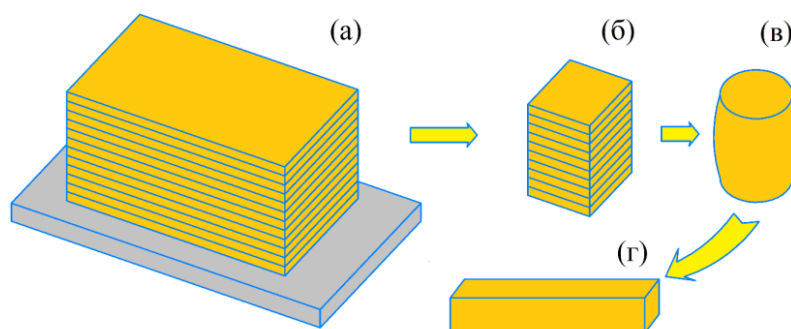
Схема получения образцов. Напечатанный на подложке материал (а) и вырезанный из него фрагмент для ИПД (б). Образцы после многостороннего прессования (в) и прокатки (г)
